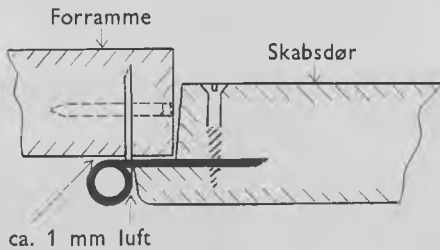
Skabsdør (til lakering), hængslet skruet fra bagsiden.
